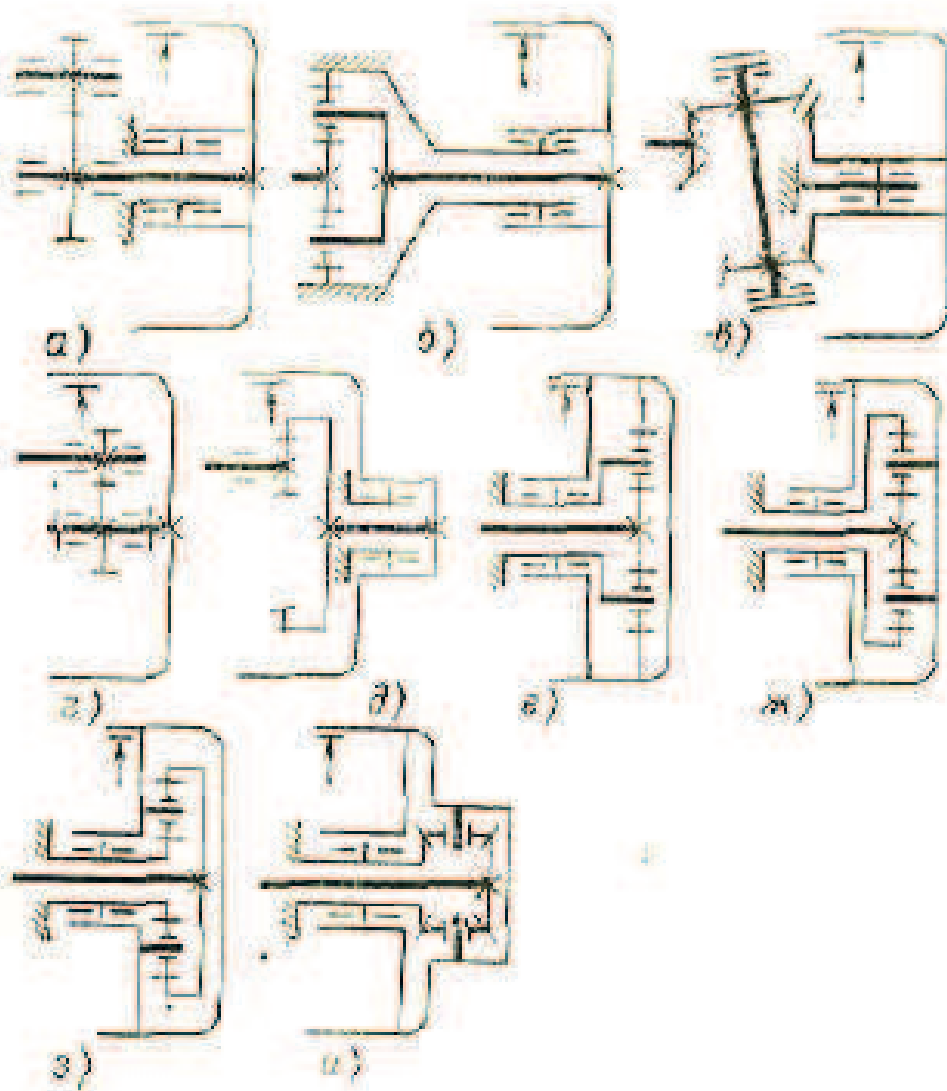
Схемы редукторов привода ведущих колес
